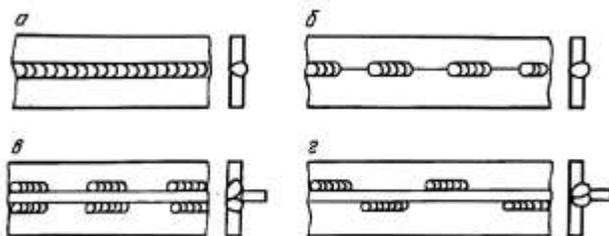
Виды сварных швов по протяженности: а – сплошной; б – прерывистый; в – цепной прерывистый; г – шахматный прерывистый
